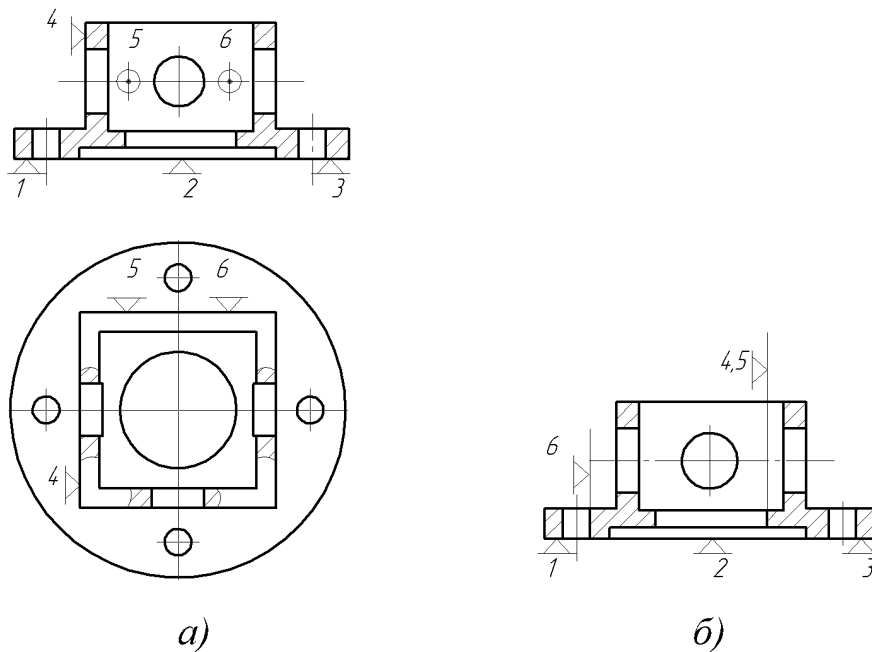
Схеми базування корпусу коробчастого типу:
